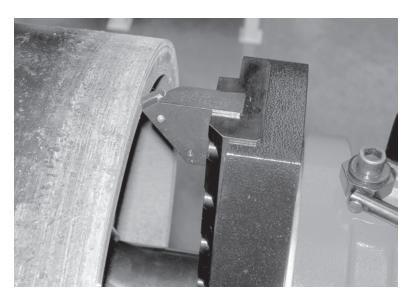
Поворачивайте ручку регулирования подачи для установки резцов рядом с обрабатываемой поверхностью трубы. Отрегулируйте положение режущих инструментов по мере необходимости.
